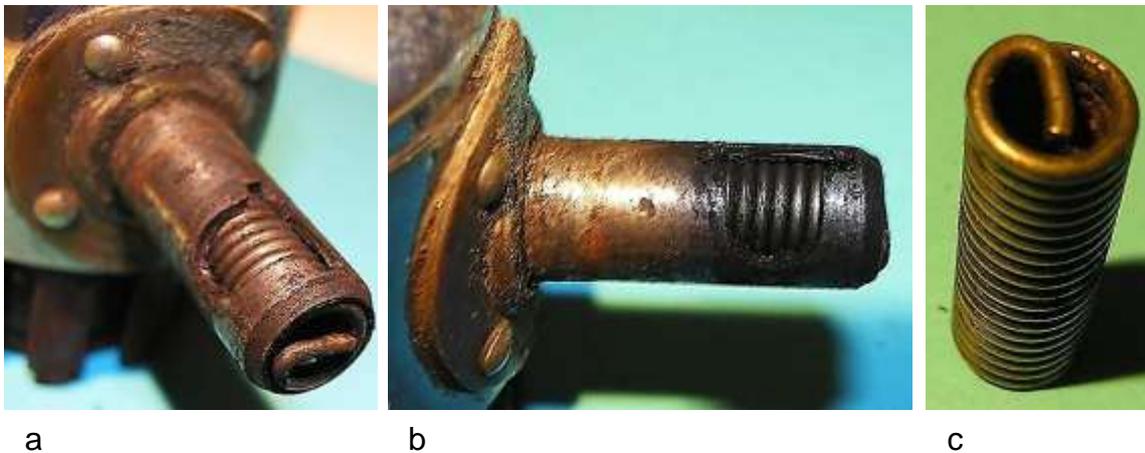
Druckfeder: a) Feder in der Drehhülse, b) Kulisser für die Arretierung, c) Druckfeder
